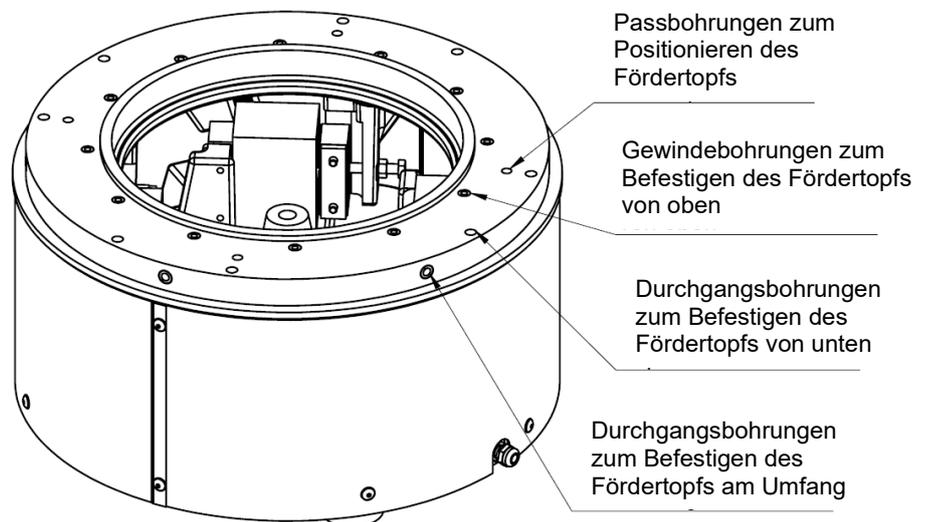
Pass- und Gewindebohrungen für die Montage des Fördertopfs
